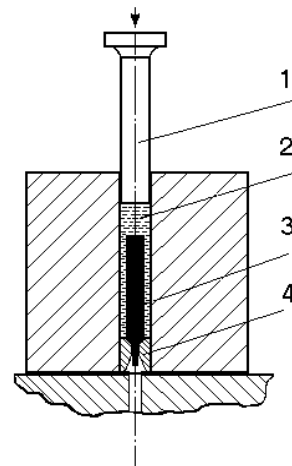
Рабочий узел для квазигидроэкструдирования: 1 — пуансон; 2 — передающая давление среда; 3 — заготовка; 4 — матрица
